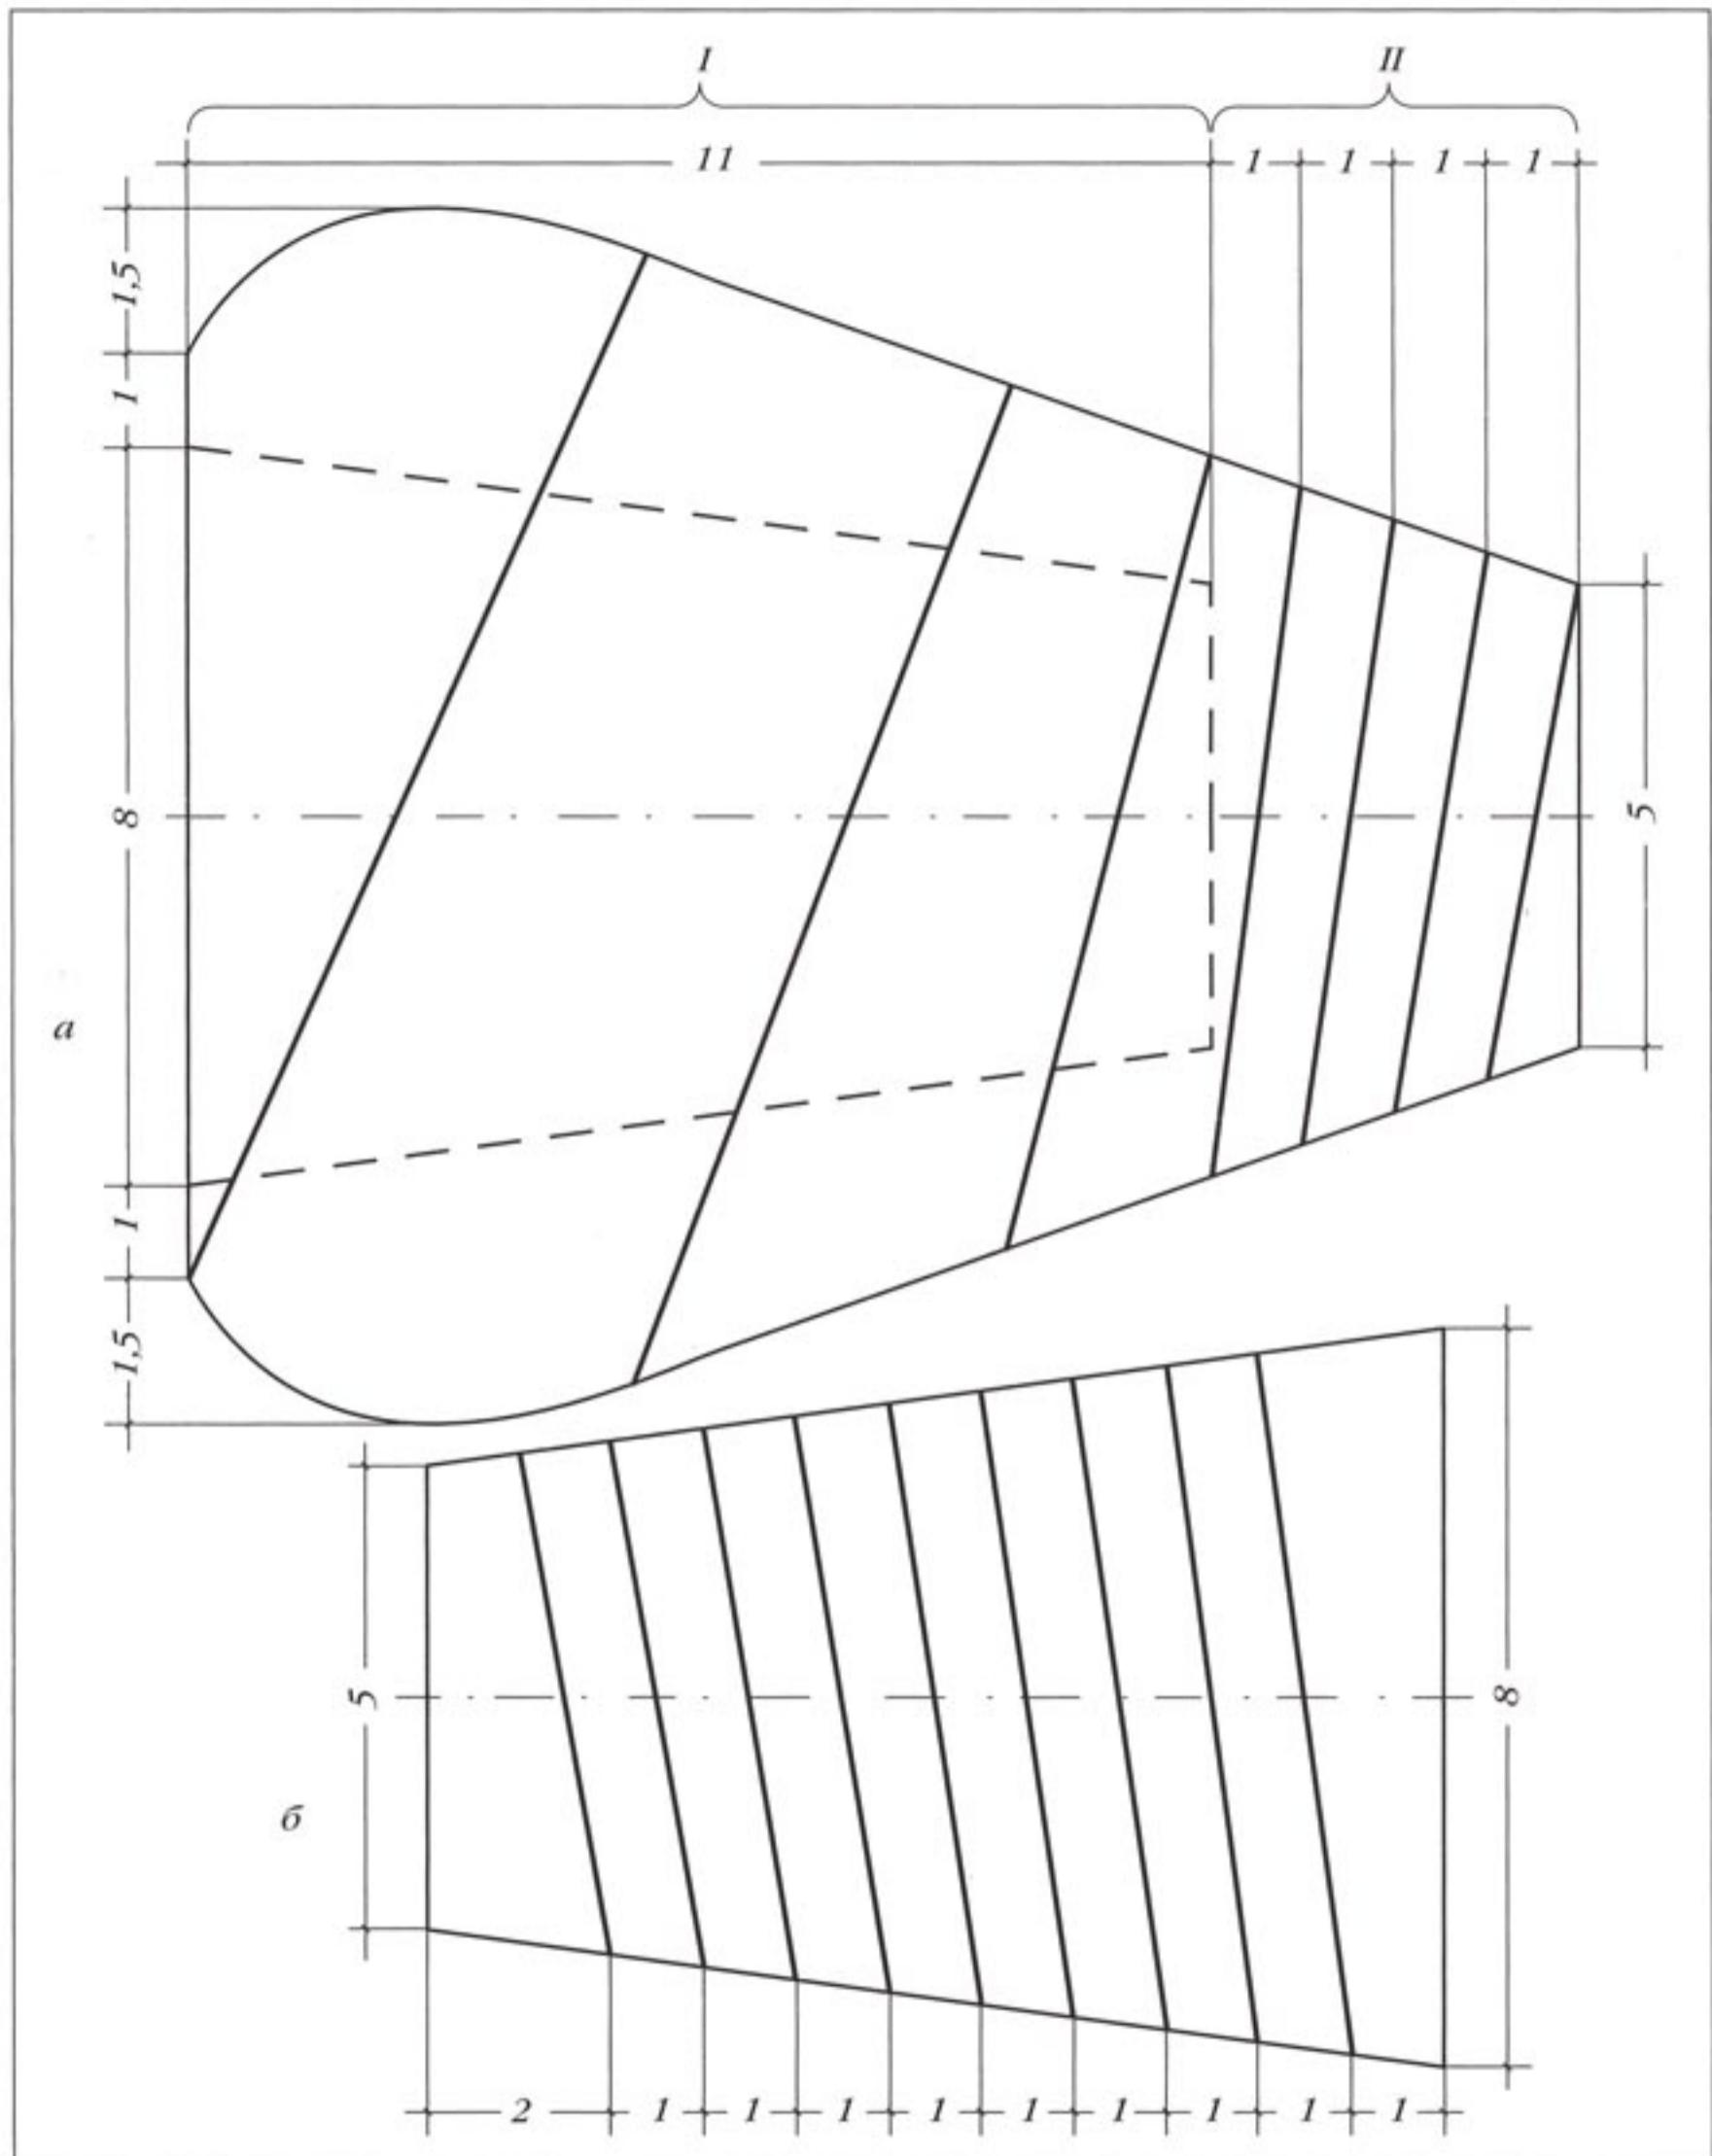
Чертеж и схема разметки деталей стойки чаши-вазы к рис. 197: *а* – внешняя деталь (*I* – шестизаходный винт, шаг 5 и 2; *II* – шестизаходный винт, шаг 1); *б* – внутренняя деталь (шестизаходный винт, шаг 1)
